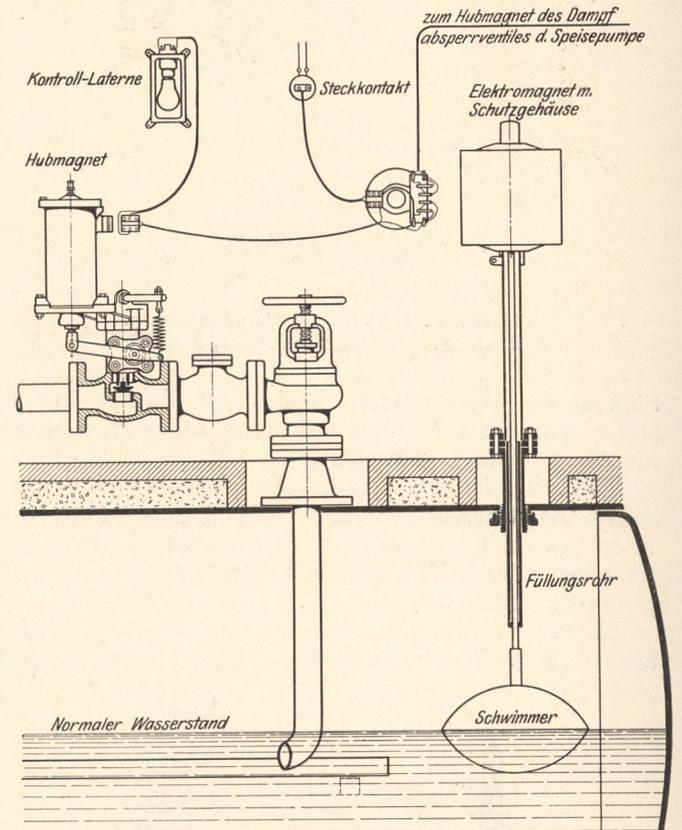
Elektrischer Wasserstandsregler, Bauart Reubold.
